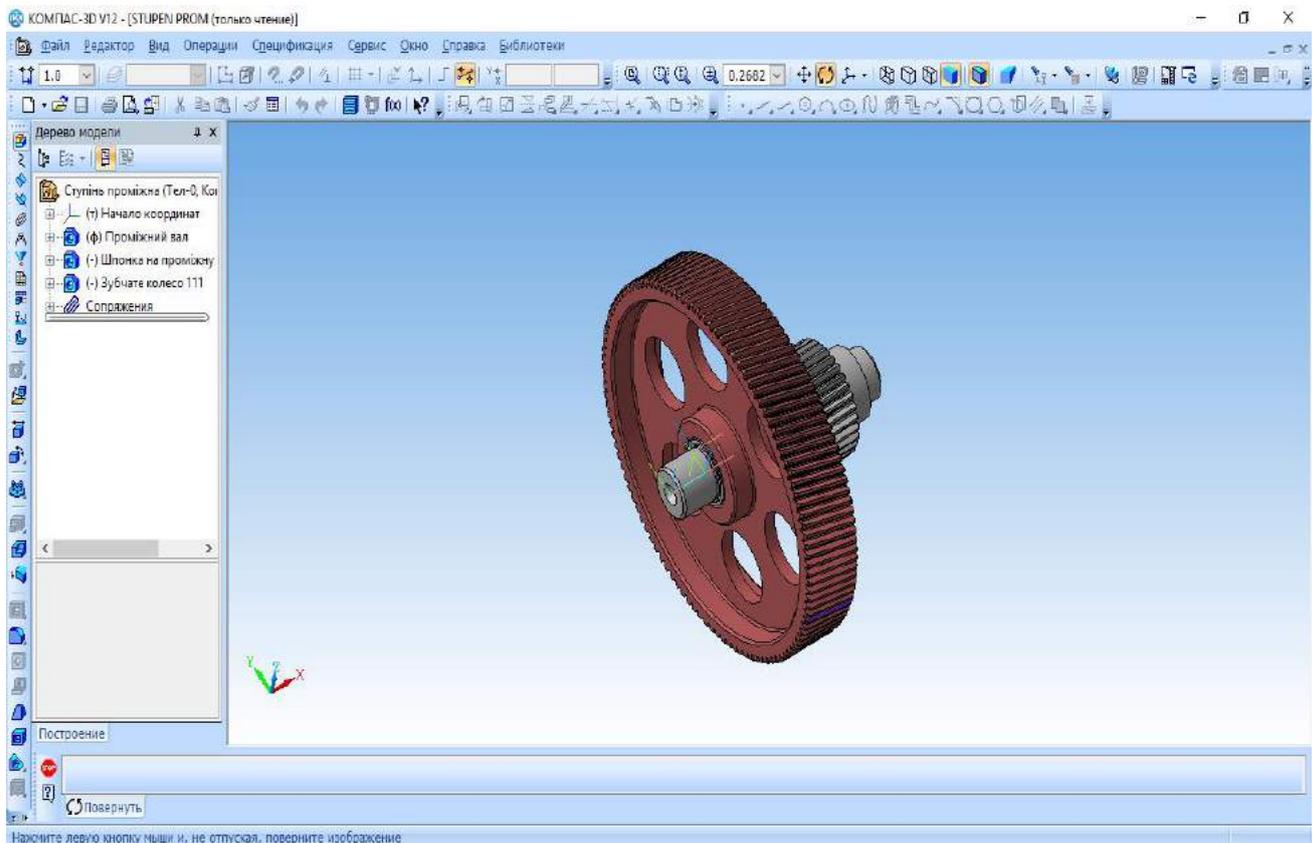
3D сборка промежуточной зубчатой передачи : вал-шестерня, колесо, шпонка
